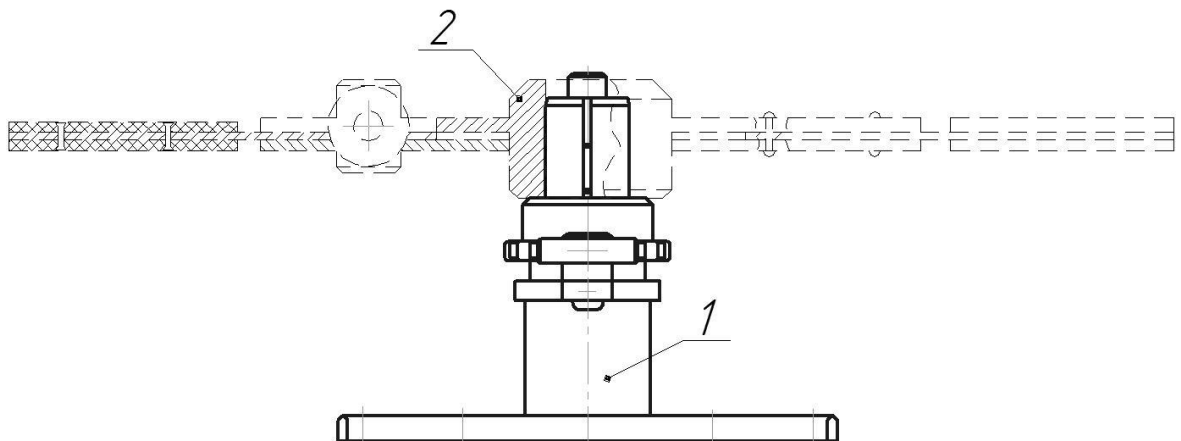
Схема встановлення веденого диска на пристрій
